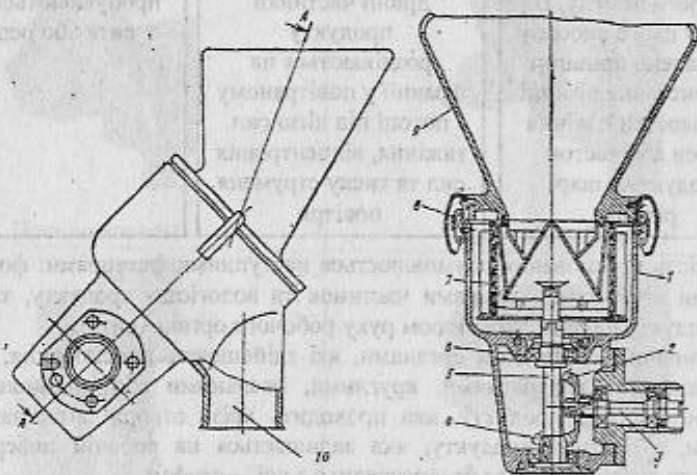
Просіювач МПП-П-І: 1 – корпус; 2 – колесо конічне; 3 – вал приводний; 4 – шестерня зубчаста; 5 – вал робочий; 6 – опори кочення; 7 – барабан-сито; 8 – засувки; 9 – воронка завантажувальна; 10 – патрубок розвантажувальний
